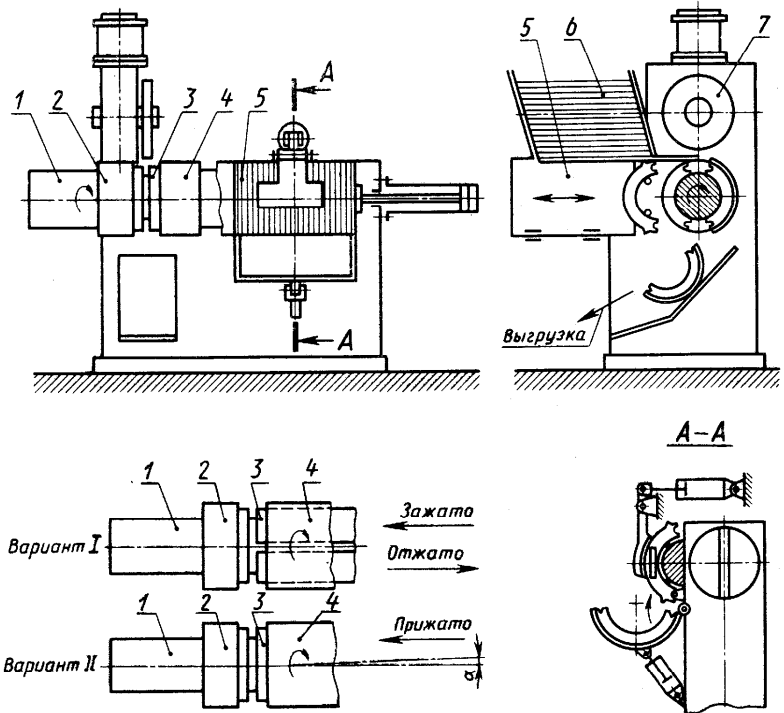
Схема работы станка-автомата для сборки и сварки тормозных колодок
